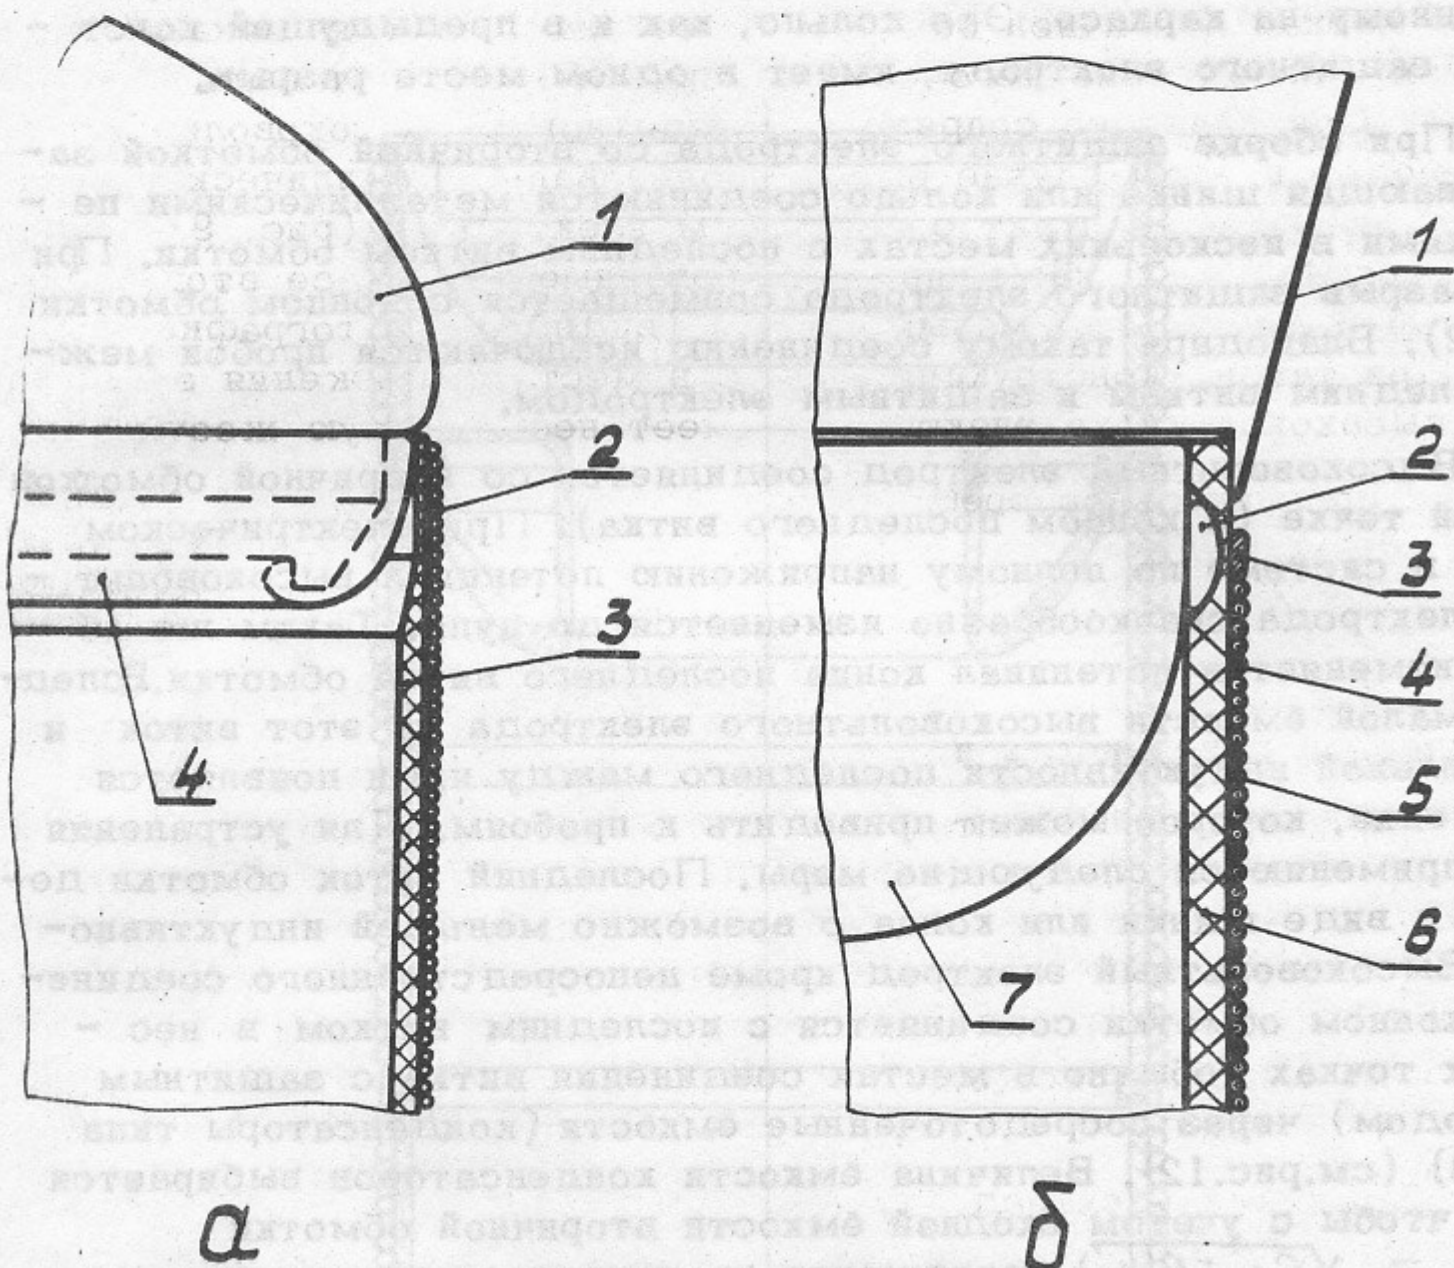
Компонировка вторичной обмотки с защитным и высоко-
